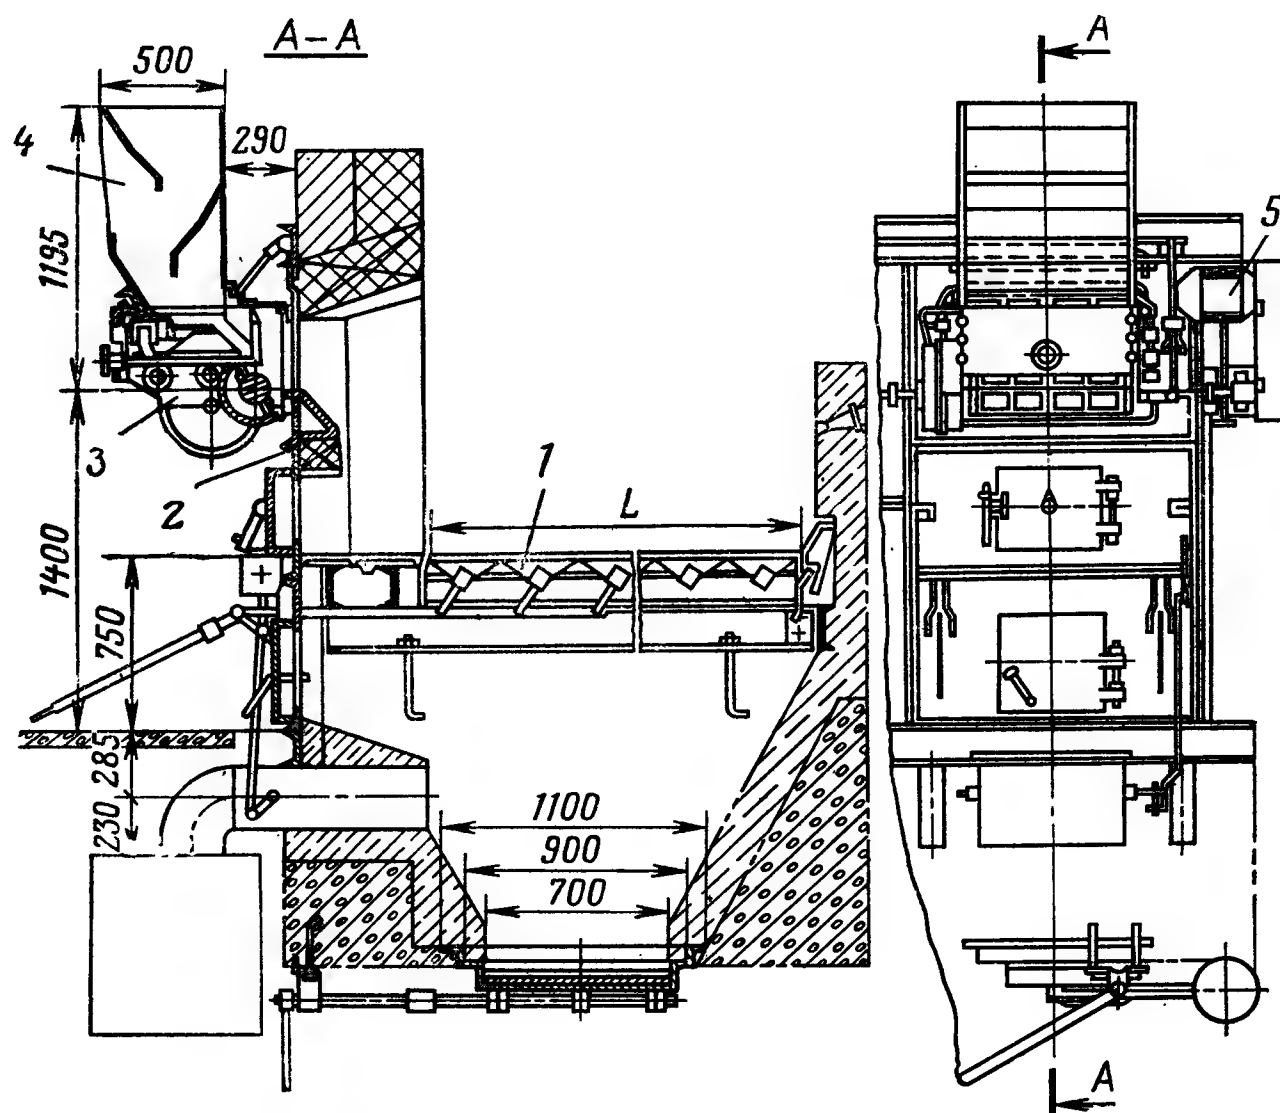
Разрез и общий вид фронта топки с ПМЗ и решеткой из поворотных колосников.
